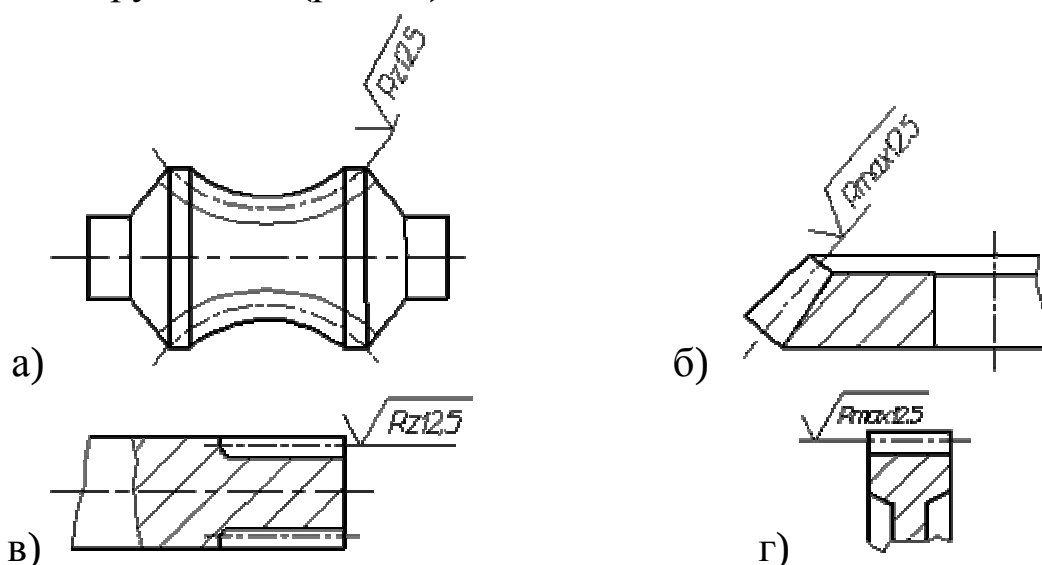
Примеры обозначения шероховатости рабочих поверхностей зубьев
